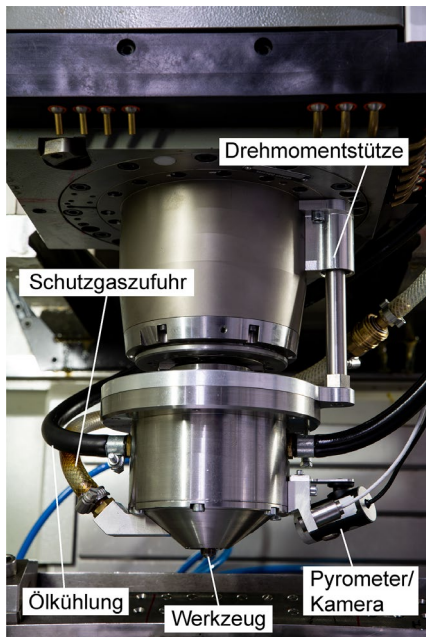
Ölgekühlter Werkzeugaufnehmer mit Schutzgasumspülung
